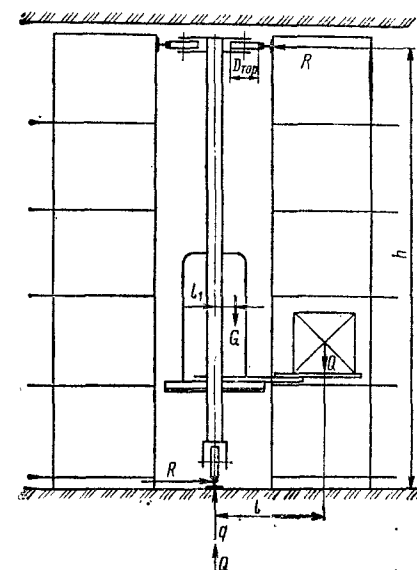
Схема к расчету механизма передвижения стеллажного крана-штабелера
